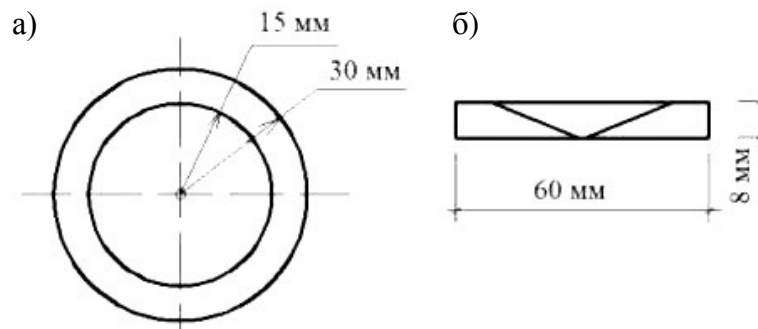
Схема конструкции марок: а – вид сверху; б – вид сбоку [Stamp design diagram: a is top view; b is side view]
